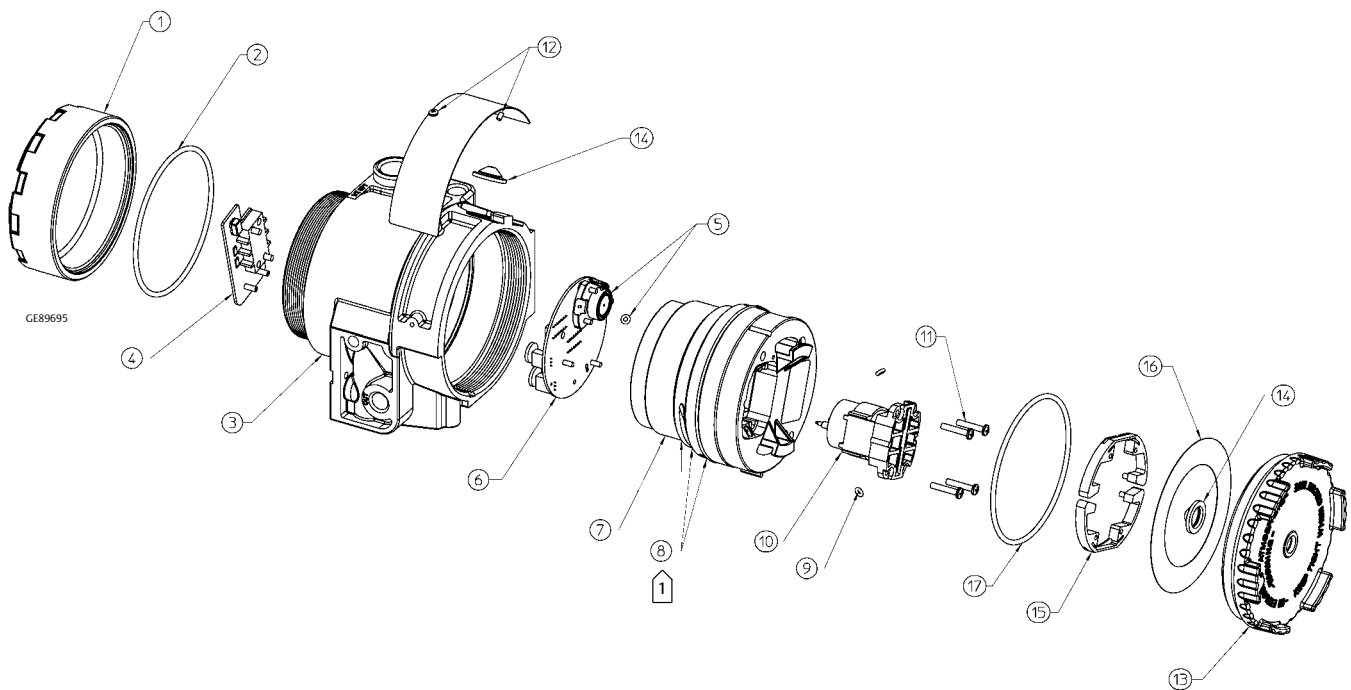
Explosionszeichnung (siehe auch Tabelle 5)
